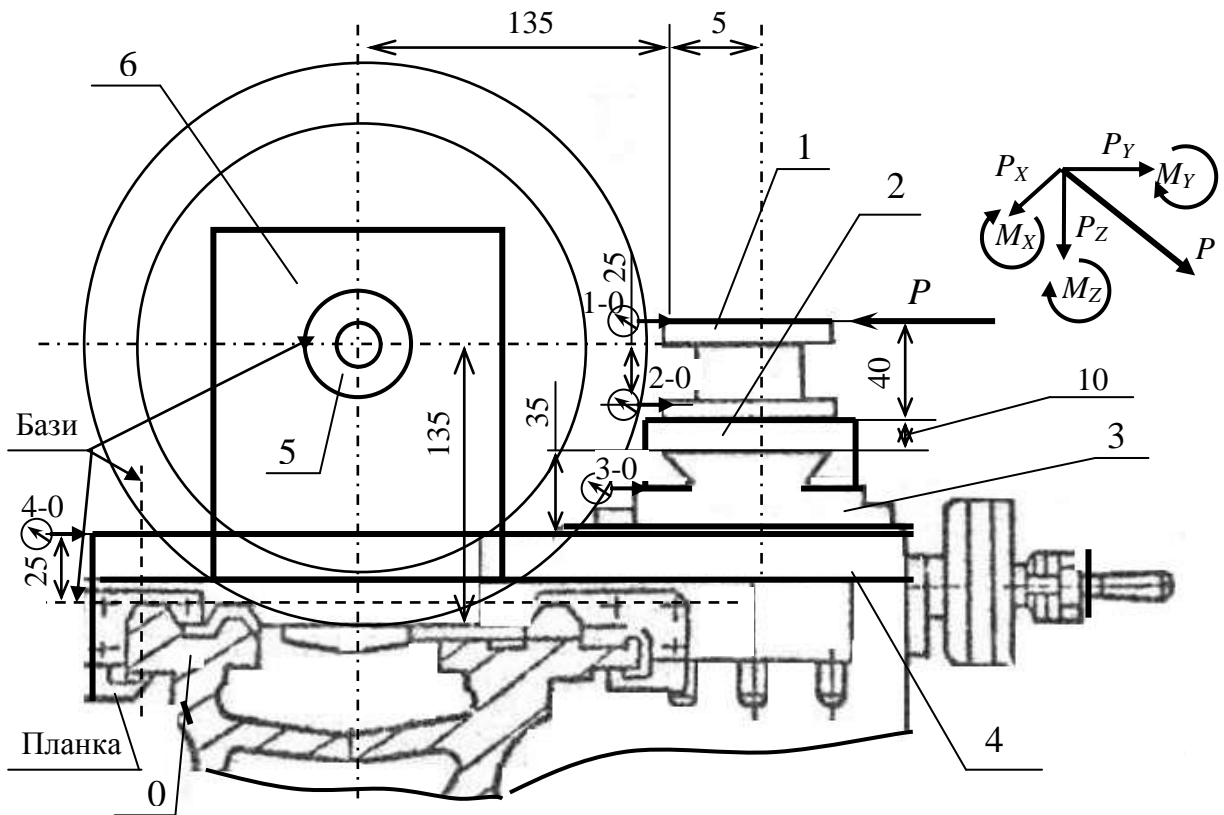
Схема навантаження і вимірів зміщень: P – навантаження; 1 – поворотний супорт; 2 – повздовжні санчата; 3 – поперечні санчата; 4 – подовжній супорт; 5 – шпиндель; 6 – передня бабка; «Бази» – вимірювальні бази по координатах для мікрометрів
